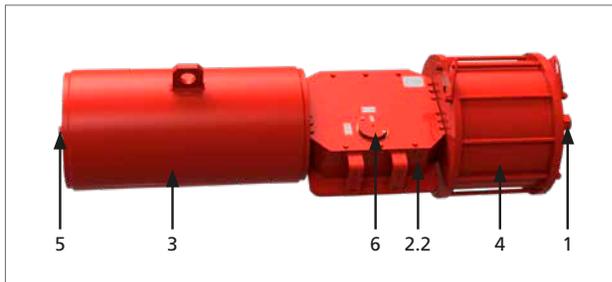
Componentes principales GPIS (cuerpo soldado)
